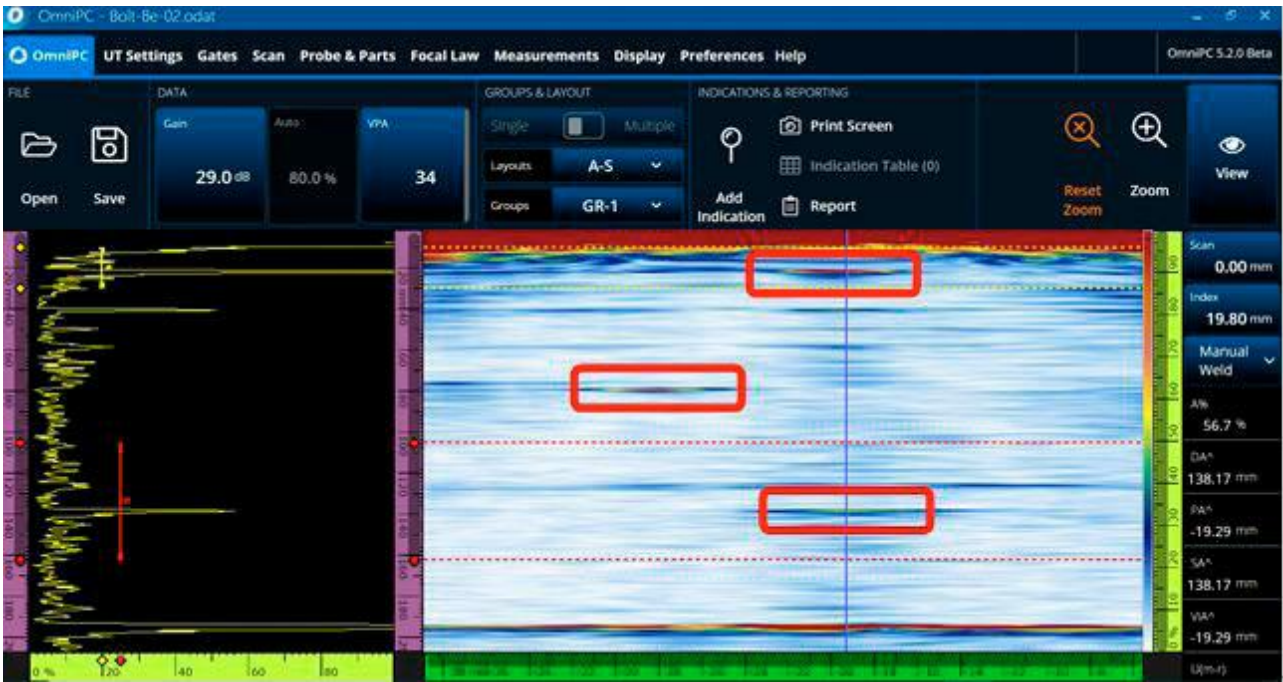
Per il difetto (scanalatura) posizionato a 140 mm dalla superficie superiore, la profondità rilevata è stata di 138,17 mm.
